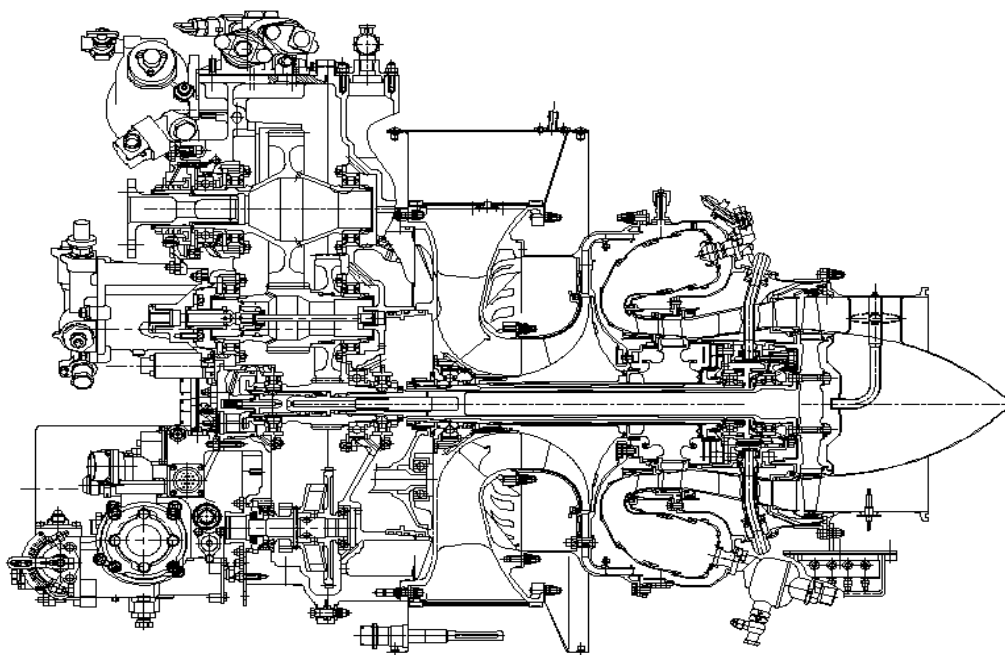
Конструктивно-компоновочная схема двигателя АИ-450
